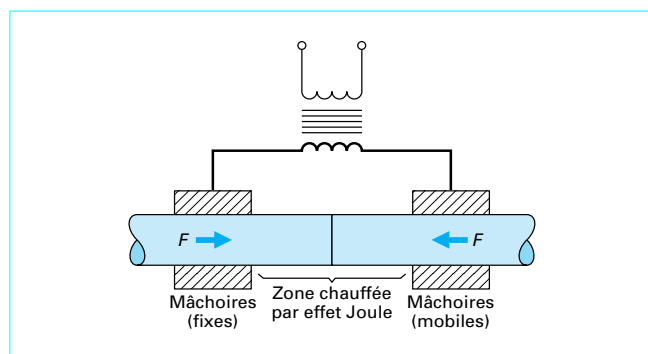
Principe du soudage électrique en bout par résistance pure, d'après [17]
